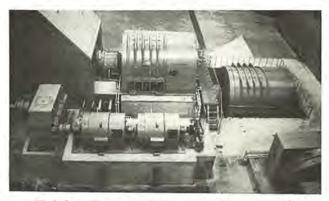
三菱 レイノルズ 熱間 アルミ 圧延機用 2-2,250 kW 主電動機 2×370 kW 巻取用電動機 2-2,250 kW main roll drive motors and 2-370 kW rewind reel motors for aluminum hot reversing mill, Mitsubishi Reynolds Aluminun Co.
